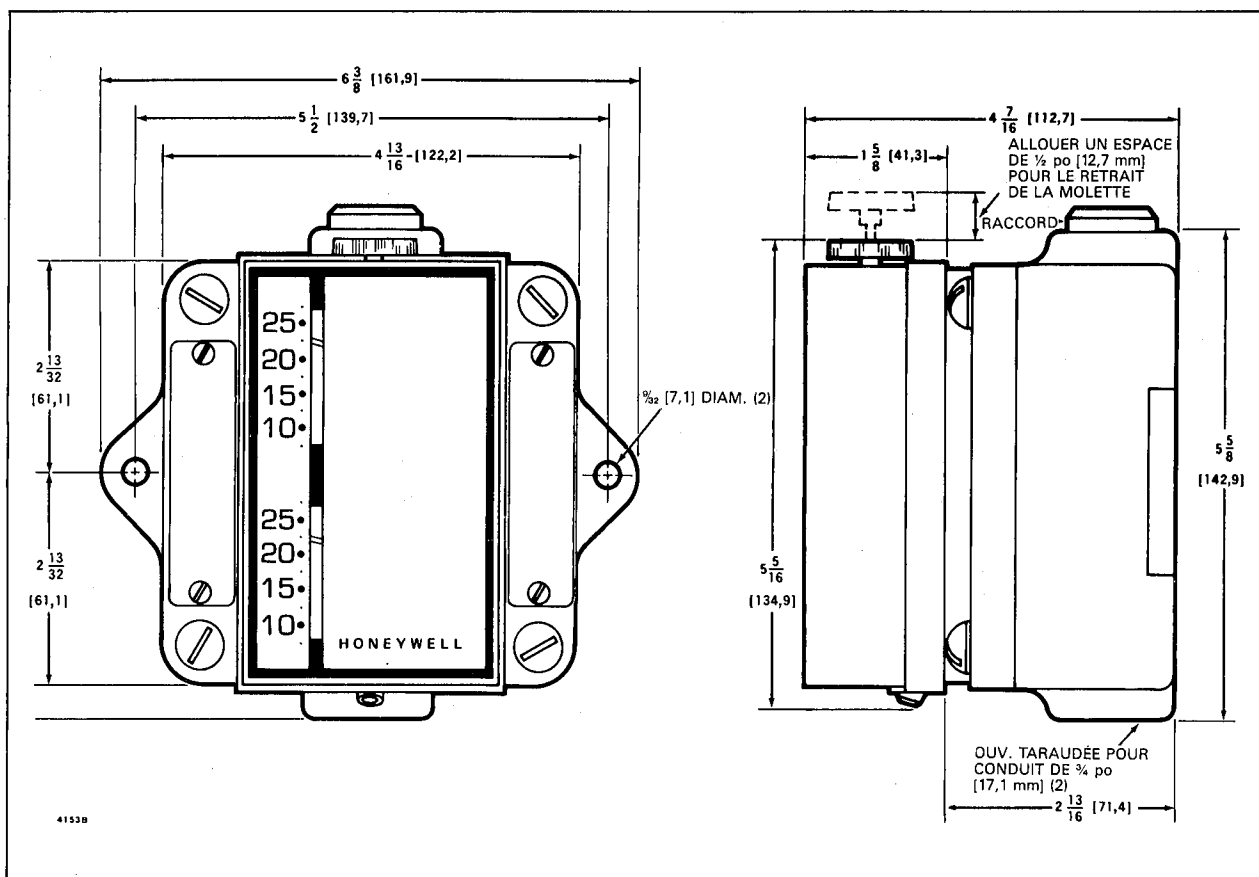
DIMENSIONS DE MONTAGE DU T6051B EN POUCES [mm].
